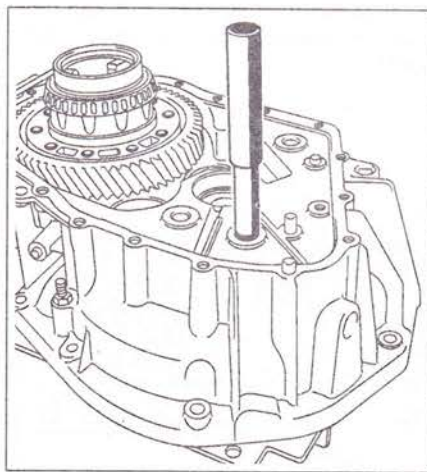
Установите подшипники при помощи приспособления В. Vi. 1510-01, индекс Q.
